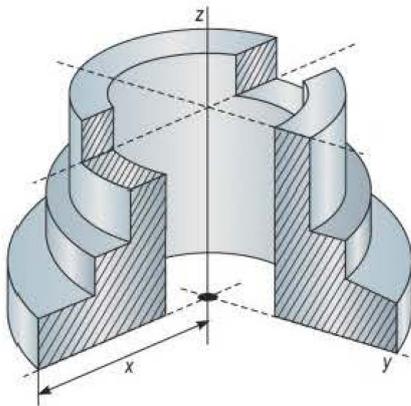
Dibujo técnico de una pieza en perspectiva, seccionada.
